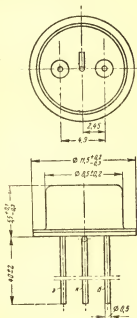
Габаритный чертеж транзисторов П414—П415Б.
